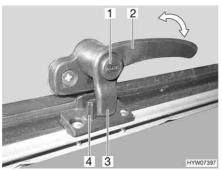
Leva di serraggio con bottone di sicurezza in posizione "Chiuso"
